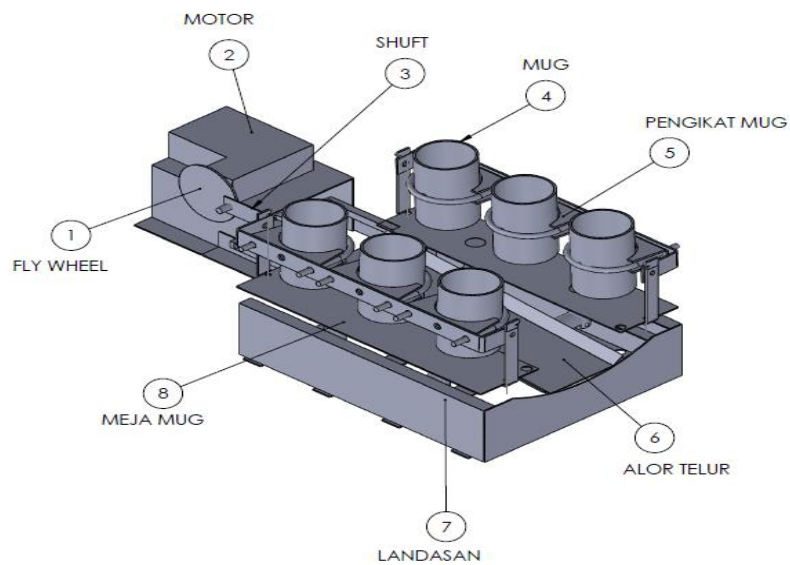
Boiled Egg Shell Breaker Machine
